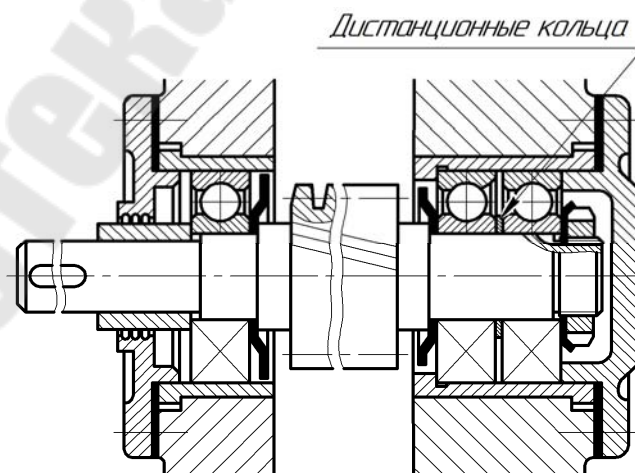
Подшипниковый узел со сдвоенными радиально-упорными шарикоподшипниками и «плавающим» радиальным шарикоподшипнике
